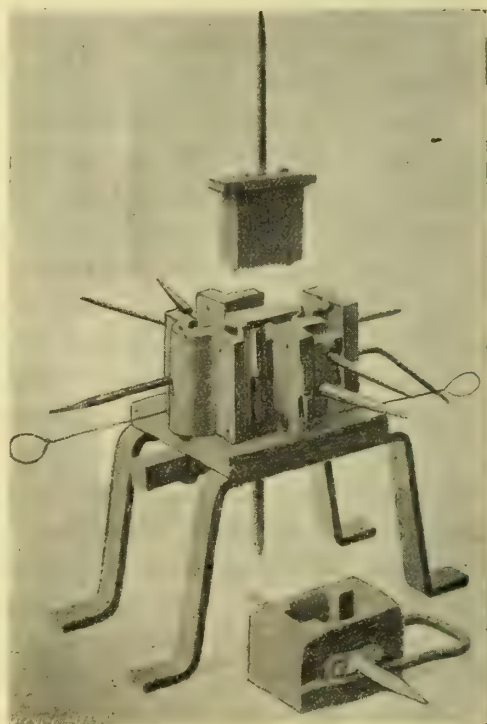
Coquille à mouler l'aluminium, ouverte.
